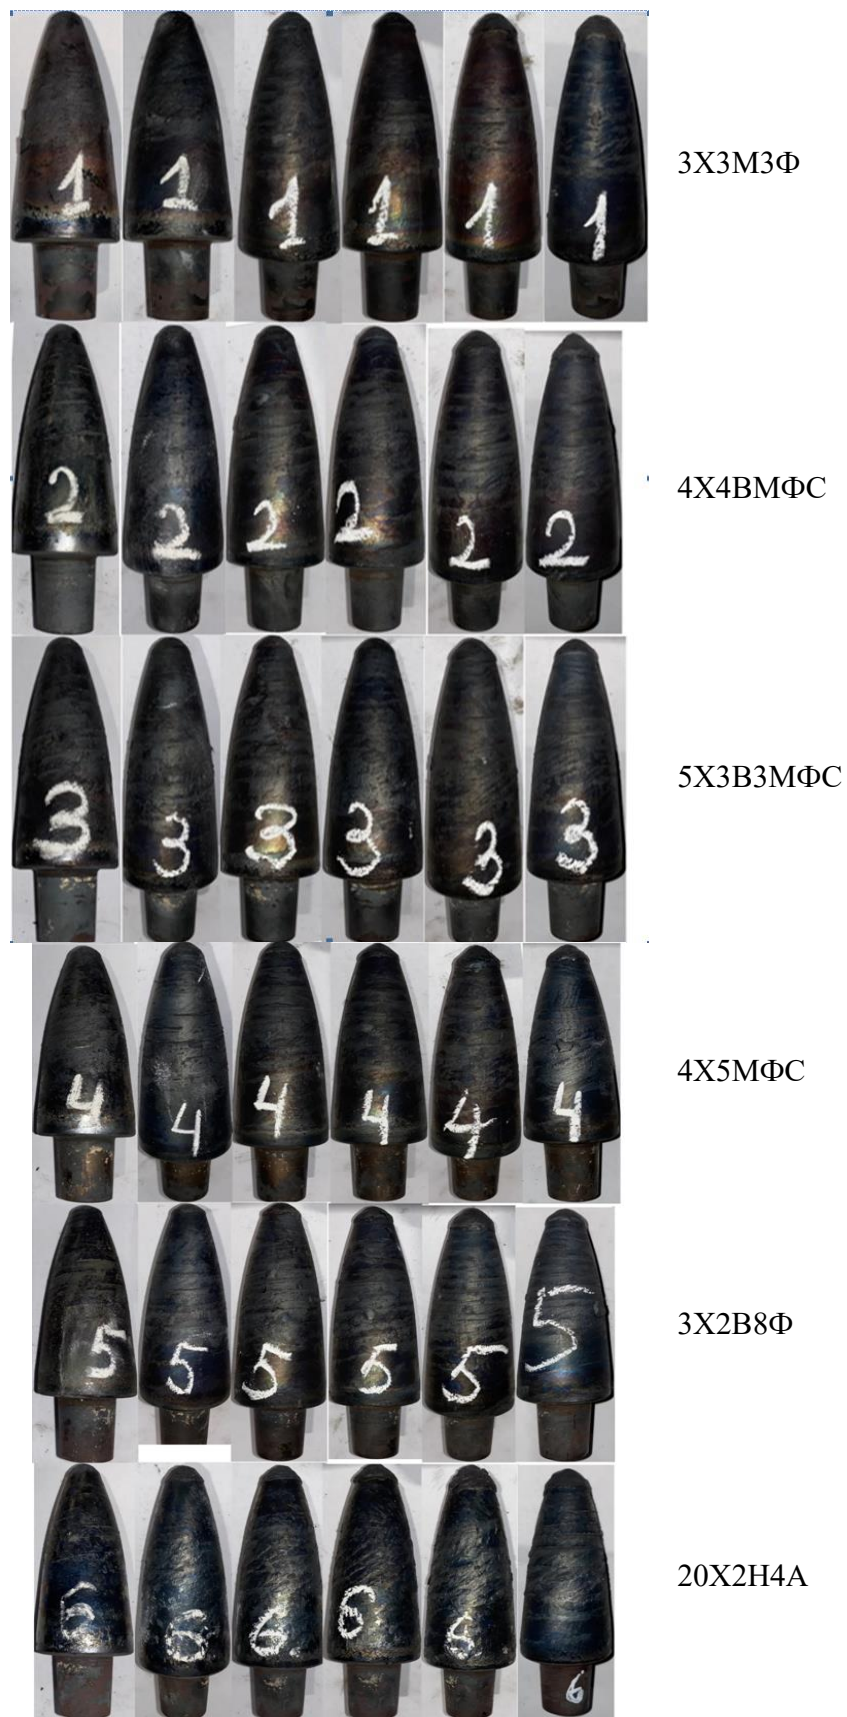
Внешний вид оправок, после прошивки 5 заготовок
